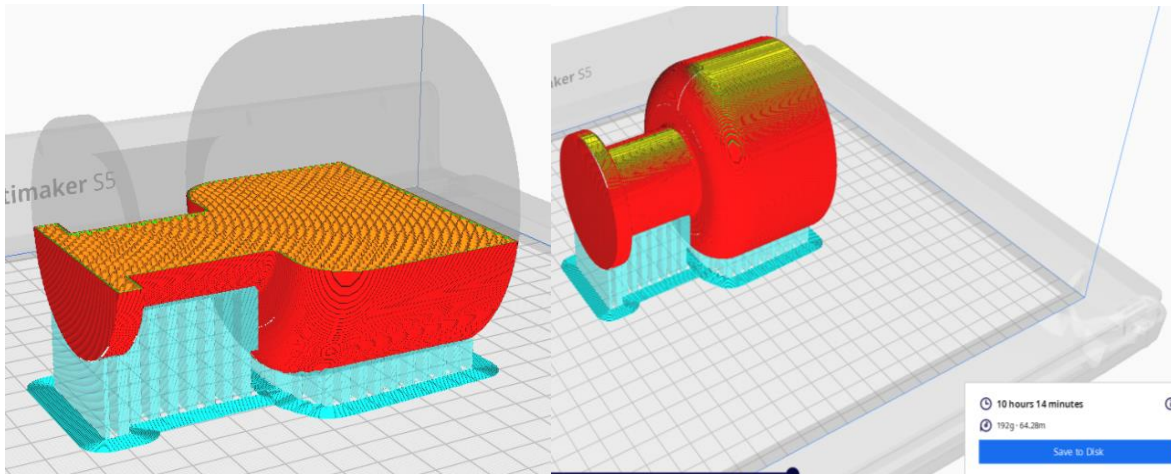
a) Densidad y soporte de la pieza a imprimir. b) Vista previa final de la pieza a imprimir.
